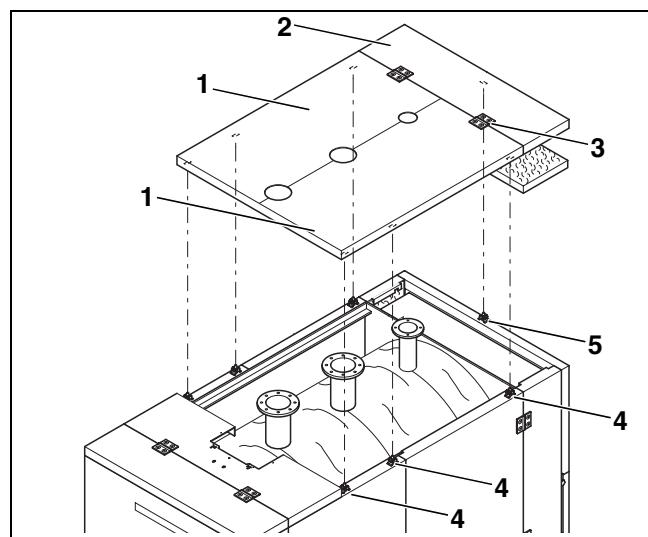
Монтаж крышек на котлах 120 - 1200 кВт
